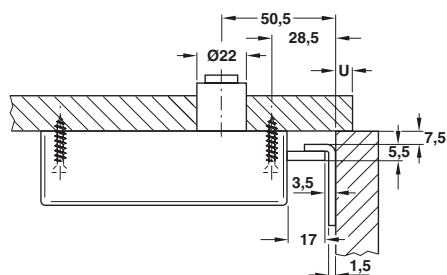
Vista dall'alto a anta battente con contropiastra ad angolo
